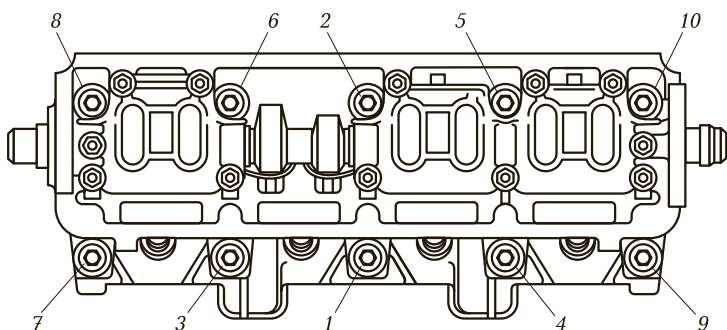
Порядок затягивания гаек [1—10] шпильчатого соединения, обеспечивающего крепление головки блока цилиндров
